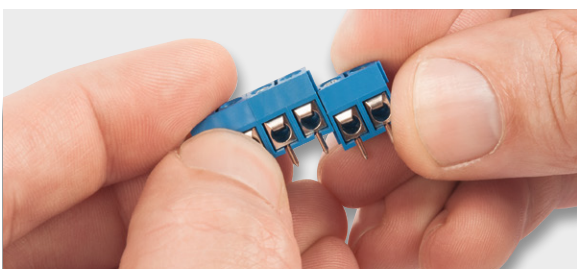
So sind die Schraubklemmen gleicher Größe zusammenzustecken.
